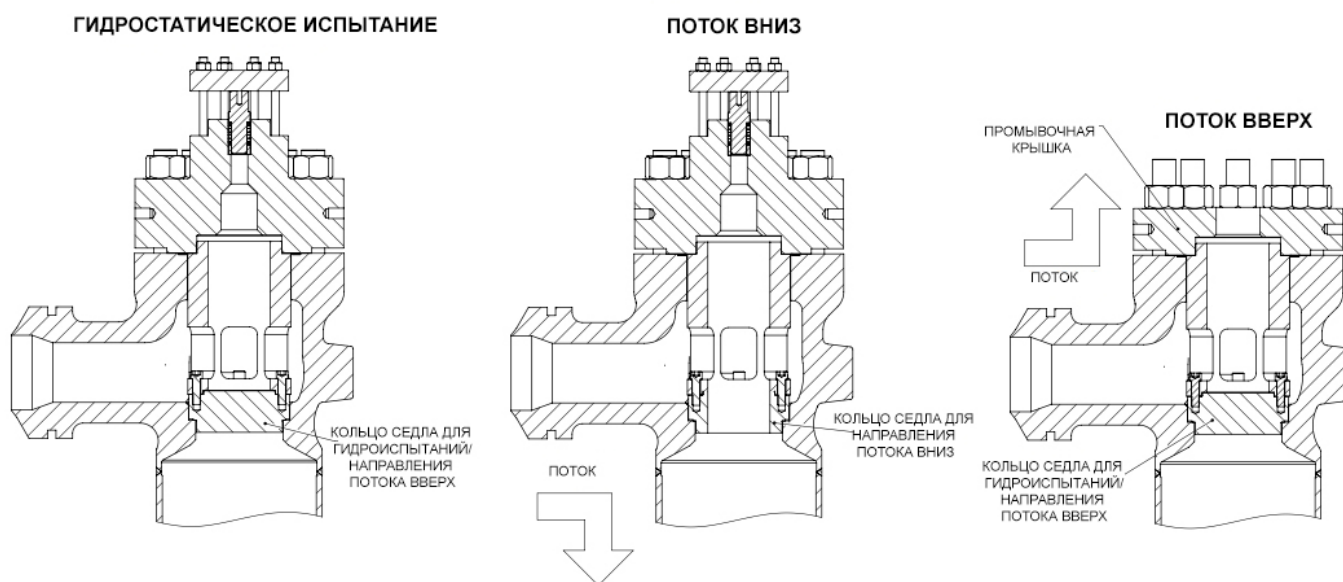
Примеры приспособлений для промывки и гидростатических испытаний
